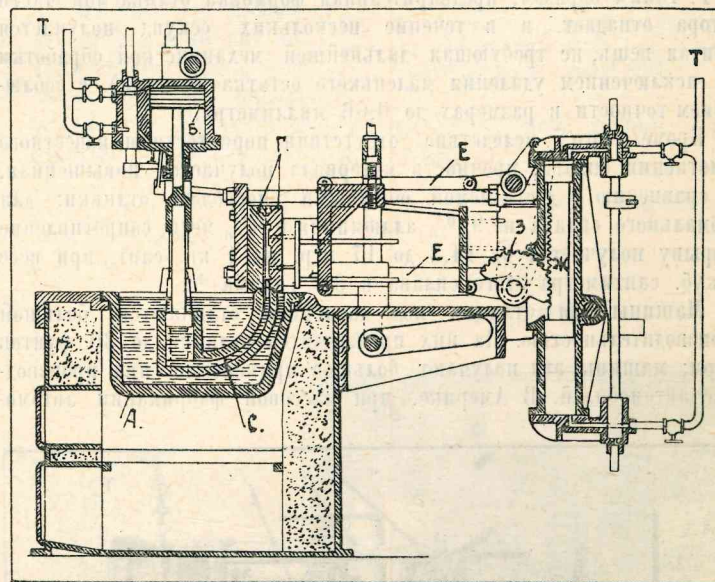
Продольный разрез автоматической машины для отливки под давлением.
